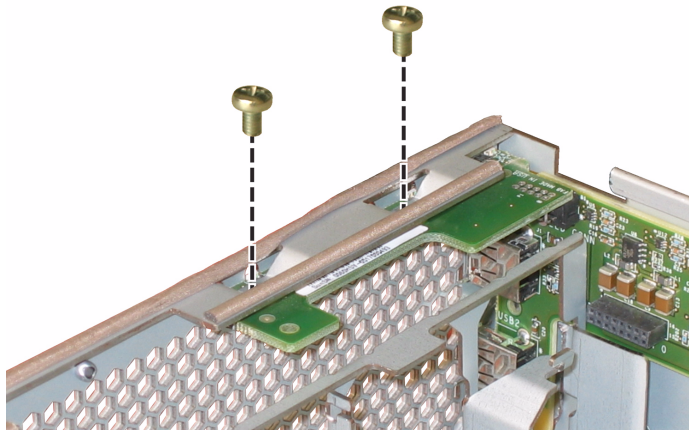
Extracción de los tornillos de la tarjeta de indicador del panel frontal
